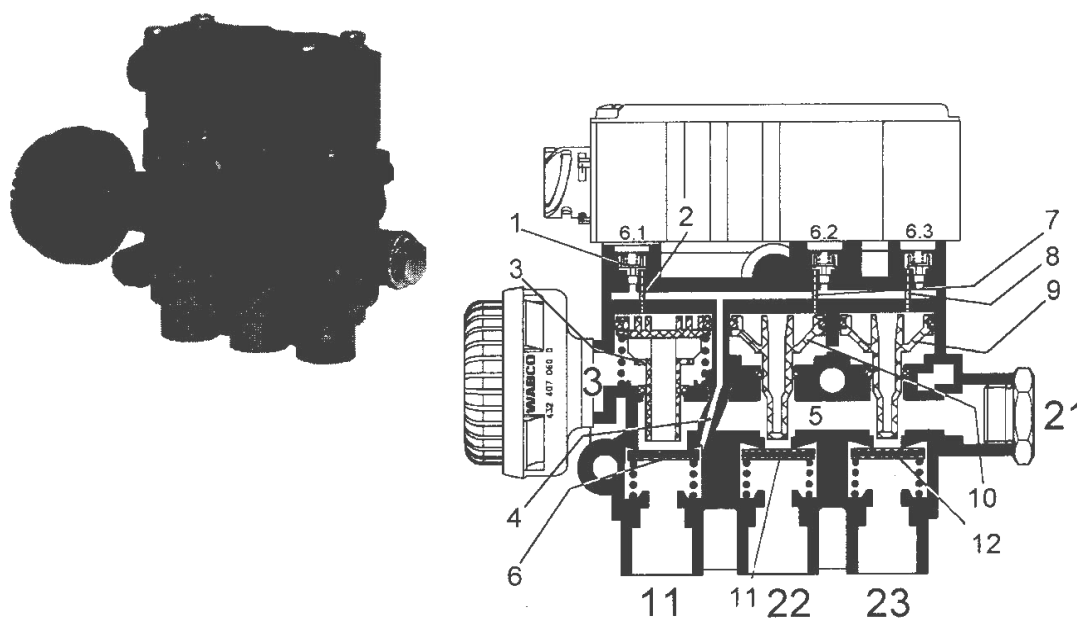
Магнитный клапан ECAS 472 900 05.0
